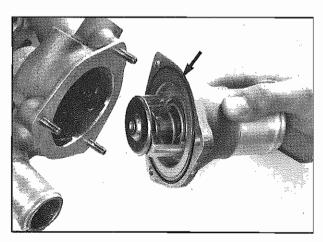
Posizione esatta foro sulla valvola Proper position of hole on valve
